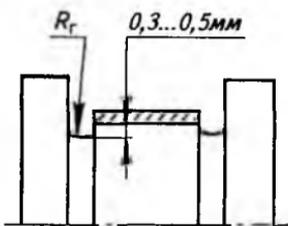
Схема наплавки шеек вала с углублением и упрочнением галтелей
